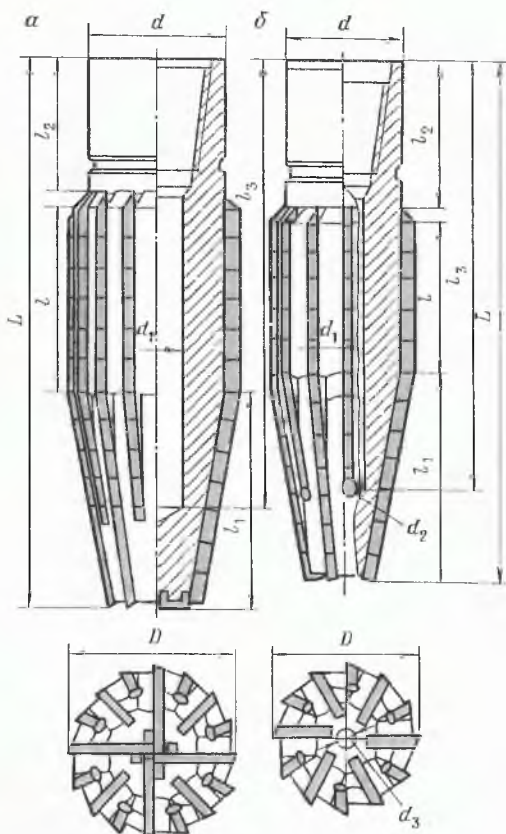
Фрезер колонный конусный (ФКК) с боковыми (а) и боковыми и центральными промывочными отверстиями (б)
